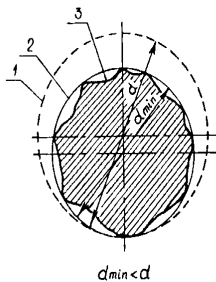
Прилегле коло для зовнішніх поверхонь обертання
